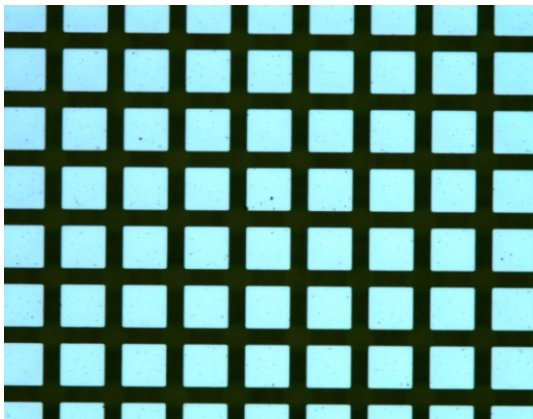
Mikroskopaufnahme der Oberfläche des Werkzeugoriginals
